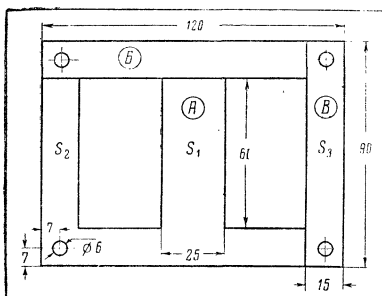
Чертеж пластины сердечника стабилизатора: А — основная пластина; Б — переключка; В — магнитный шунт
